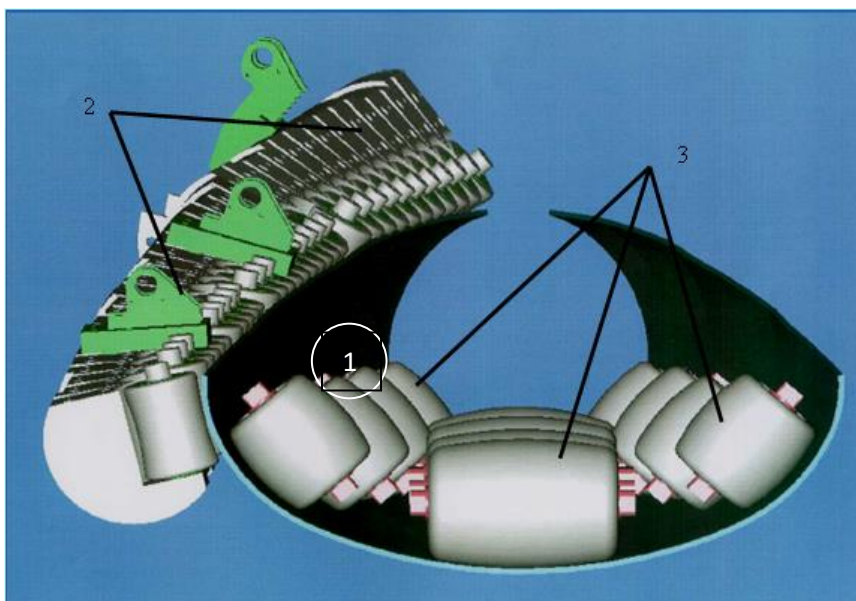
Схема расположение роликового инструмента на участке линейной формовки: 1 – трубная заготовка; 2 – боковые роликовые балки; 3 – верхние валковые сборки.
